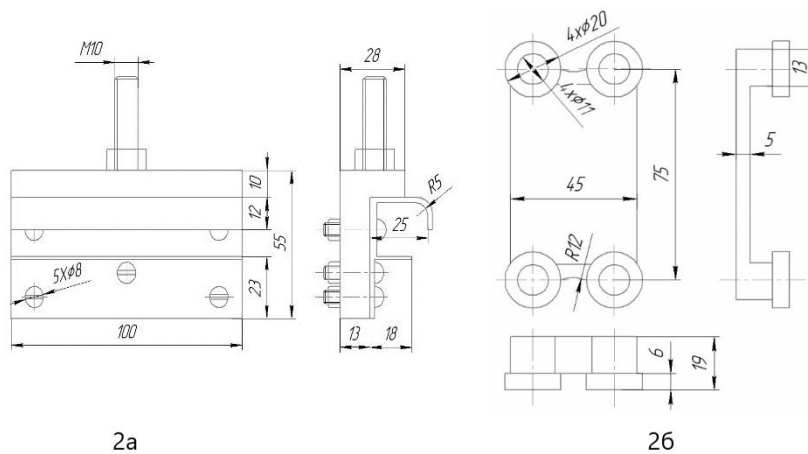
Схематичный чертёж каретки с роликами и рельсов
